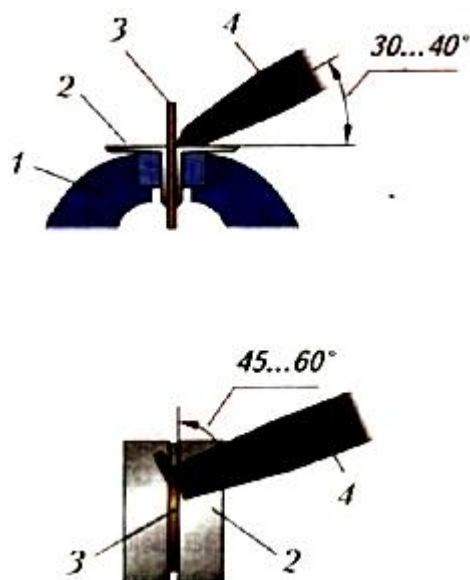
Положение зубила при рубке в тисках: 1 — тиски; 2 — нагубники; 3 — заготовка; 4 — зубило
